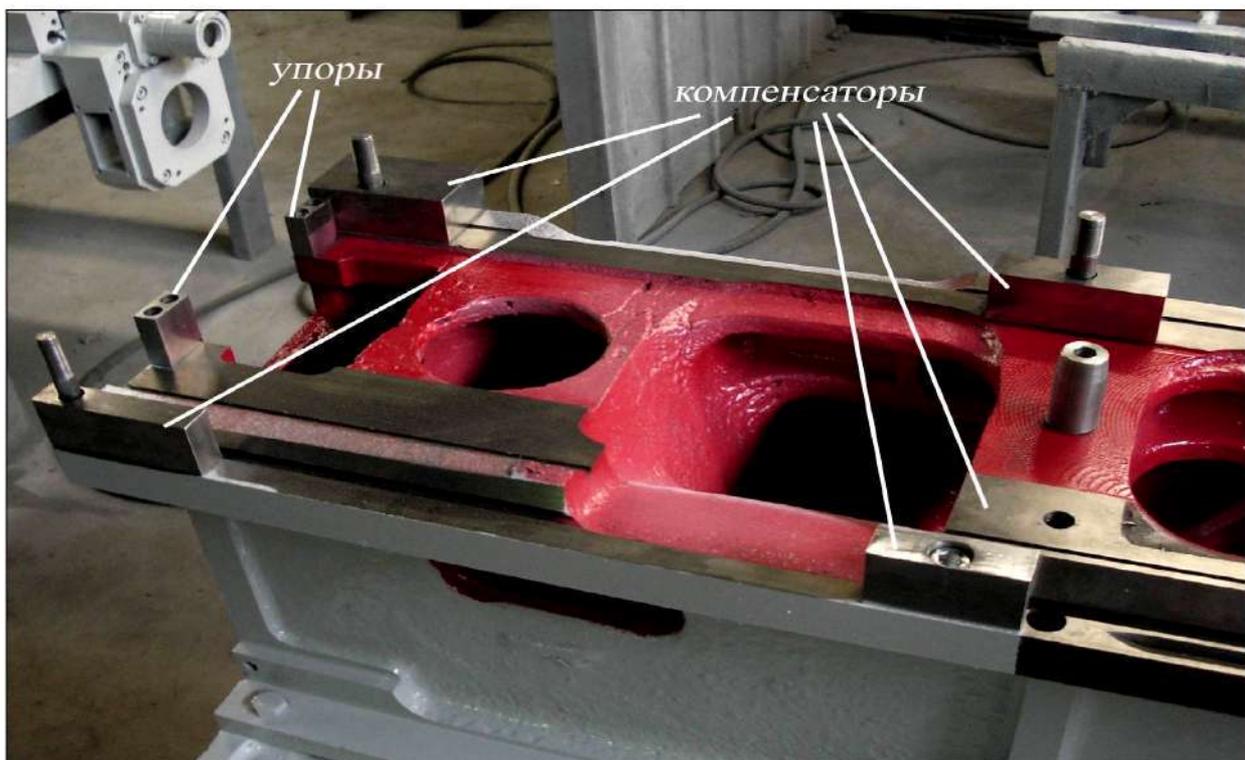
Установка компенсаторов и упоров под переднюю бабку.
